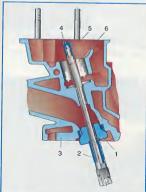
Запрессовка направляющей втулки клапана двигателя "Самары": 1 – опорная втулка; 2 – гайка; 3 – головка блока цилиндров; 4 – наконечник; 5 – шпилька; 6 – втулка клапана.
